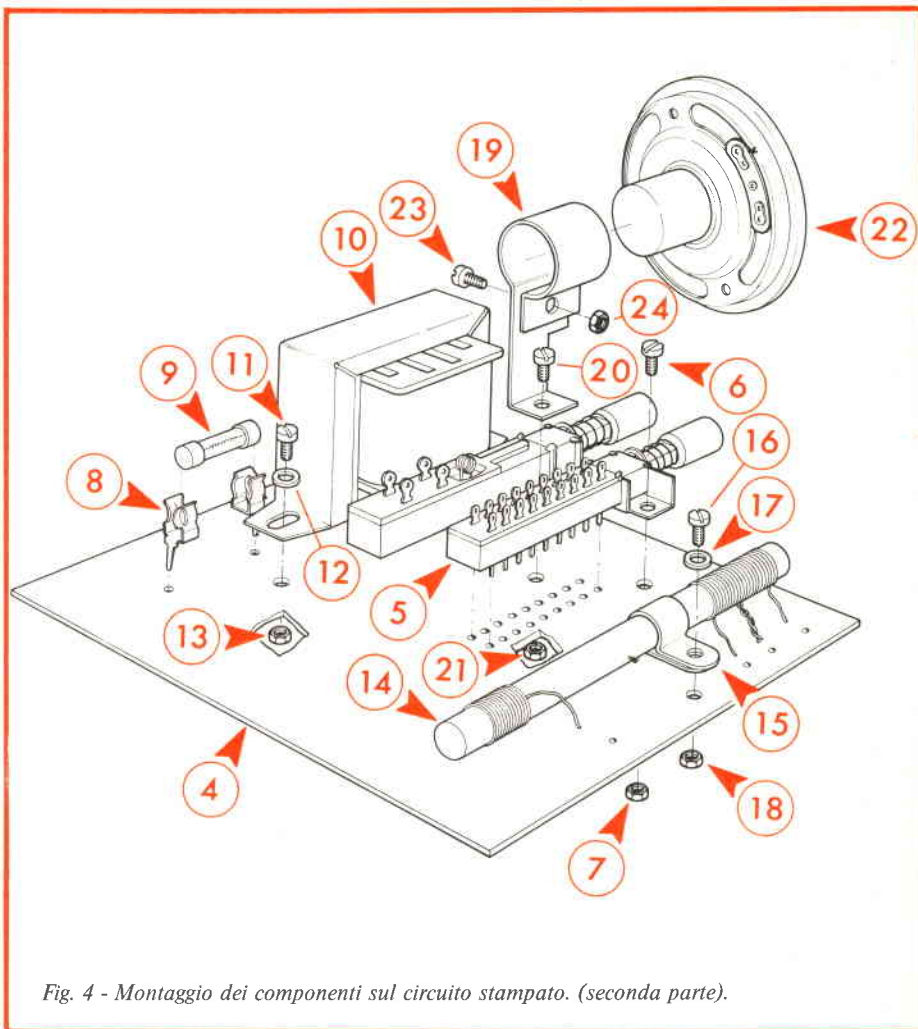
Montaggio dei componenti sul circuito stampato. (seconda parte).
